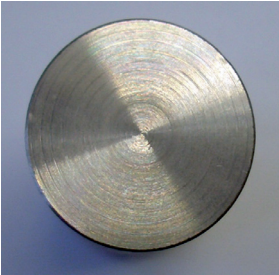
Oberfläche des Zylinderzugprüfkörpers aus Edelstahl. Der Prüfkörper wurde an der Drehmaschine bearbeitet. Im Erscheinungsbild kann er einem Punkthalter entsprechen.
